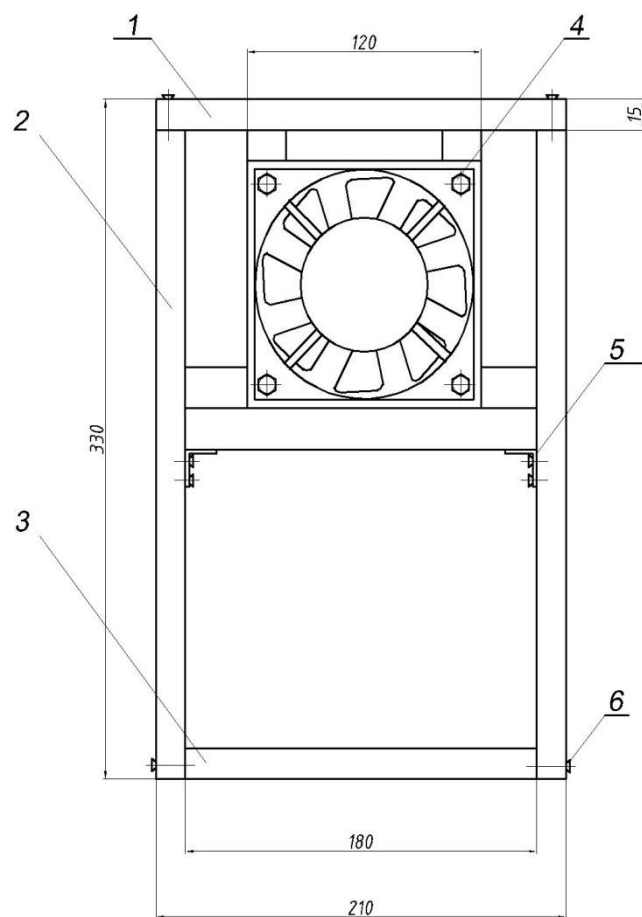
Туннель с металлическими пластинами: 1 – крышка; 2 – стенка; 3 – дно; 4 – вентилятор; 5 – металлический уголок; 6 – винты
